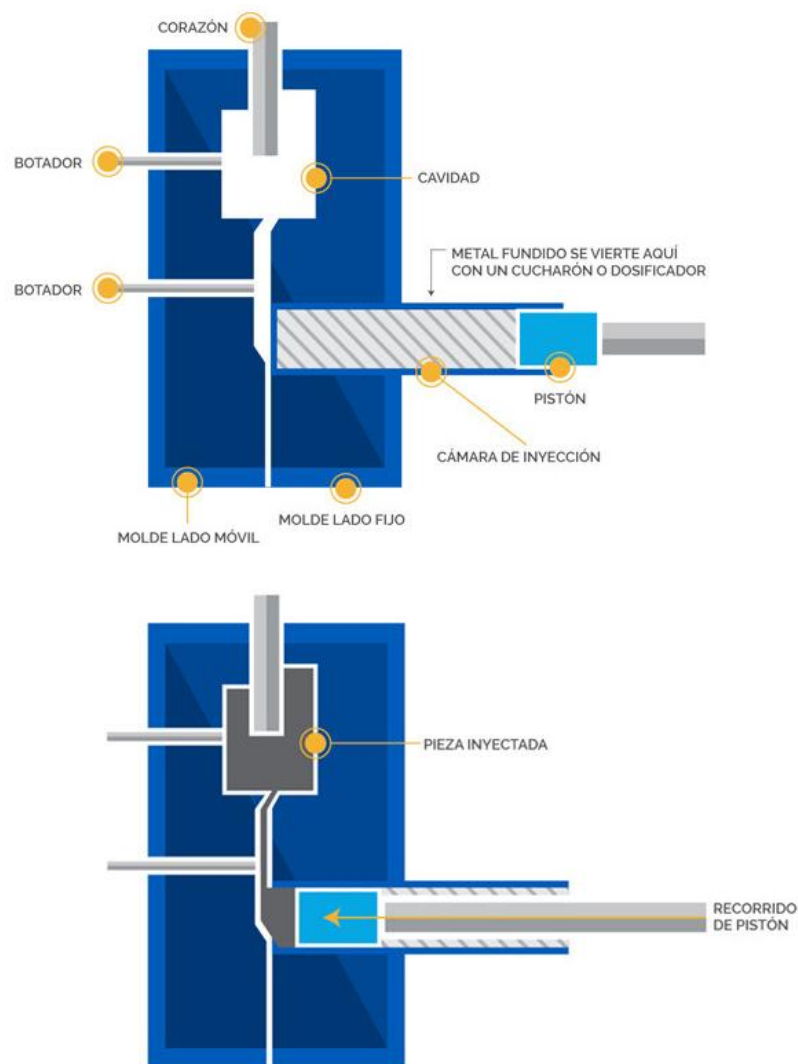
Proceso de inyección de metal en el molde. Fuente: dynacast.com
